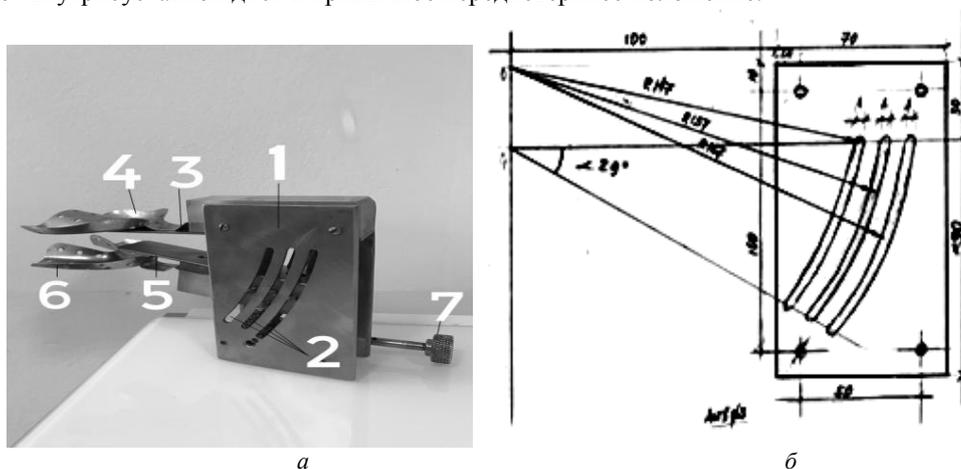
Устройство Н. М. Ватаманюка для определения межальвеолярной высоты, центрального соотношения челюстей и его чертеж: а – принципиальная модель устройства; б – чертеж для изготовления корпуса предложенного устройства
